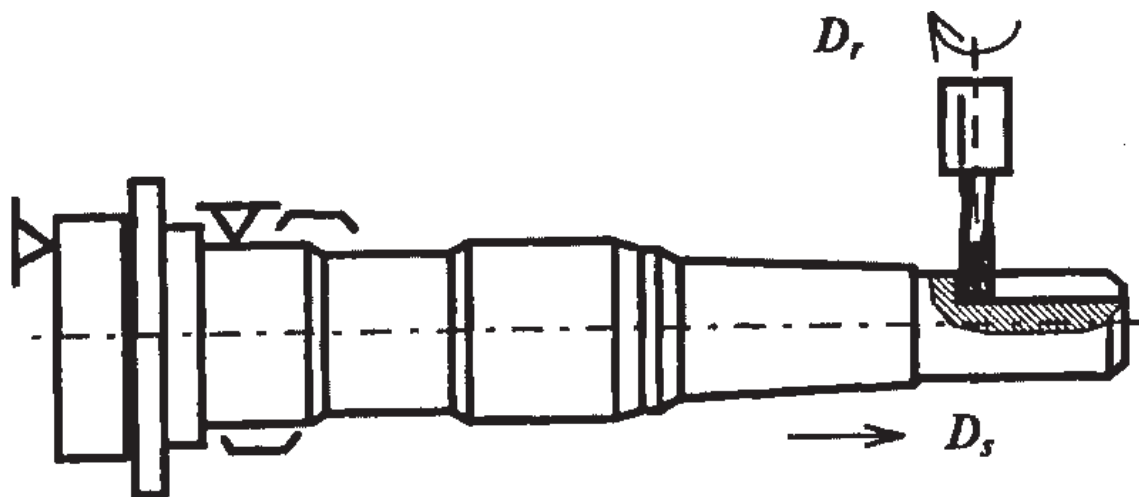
Схема фрезерования шпоночного паза на вертикально-фрезерном станке
